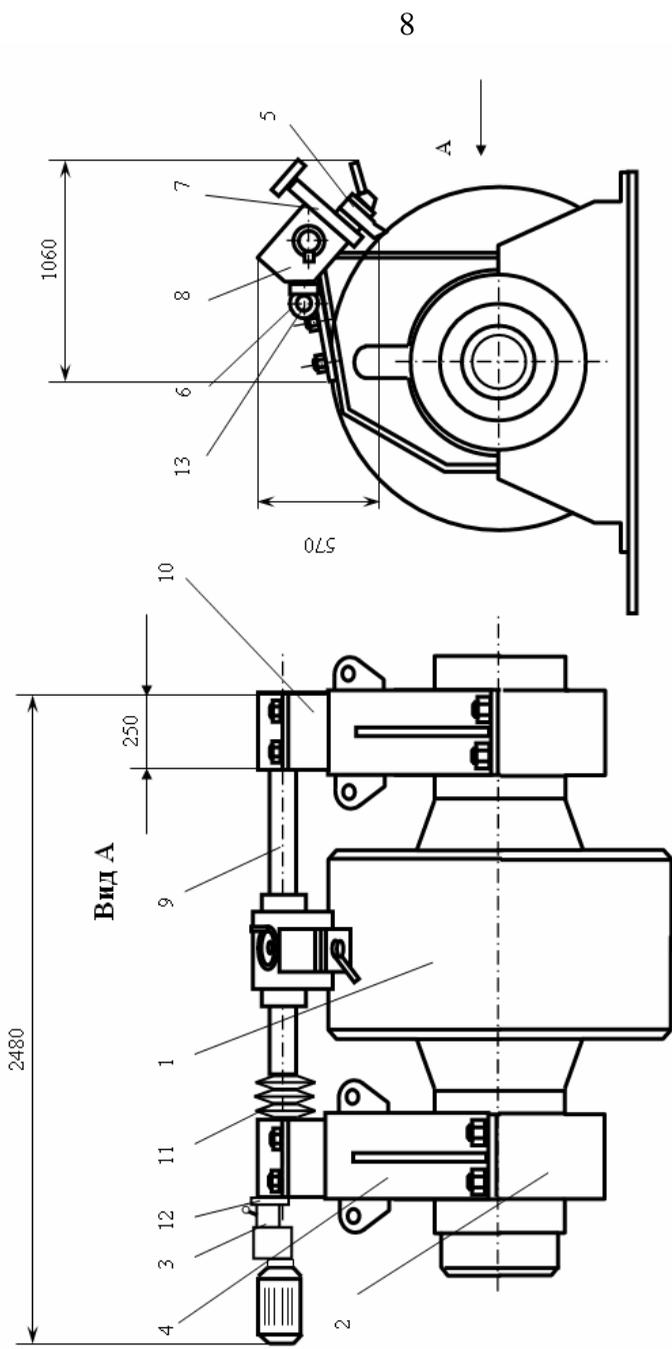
Общий вид универсального встраиваемого станка для восстановления работоспособности опорных роликов цементных печей
